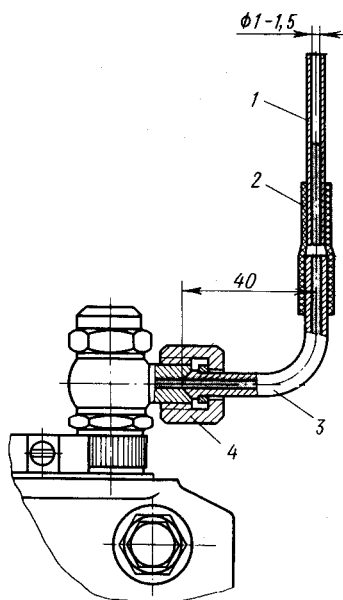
Stand de control și reglare a pompelor instalației de alimentare MAC:
